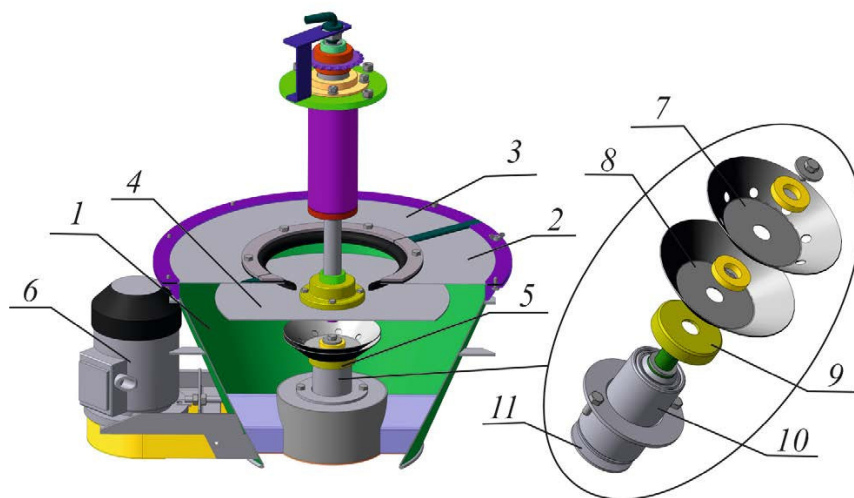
Камера протравливания: 1 – корпус камеры протравливания; 2 – полукрышка съемная; 3 – полукрышка фиксированная; 4 – распределительный диск; 5 – многодисковый распылитель на опоре; 6 – привод многодискового распылителя; 7 – верхний диск с отверстиями; 8 – нижний диск; 9 – отражатель; 10 – опора в сборе, 11 – шкив
